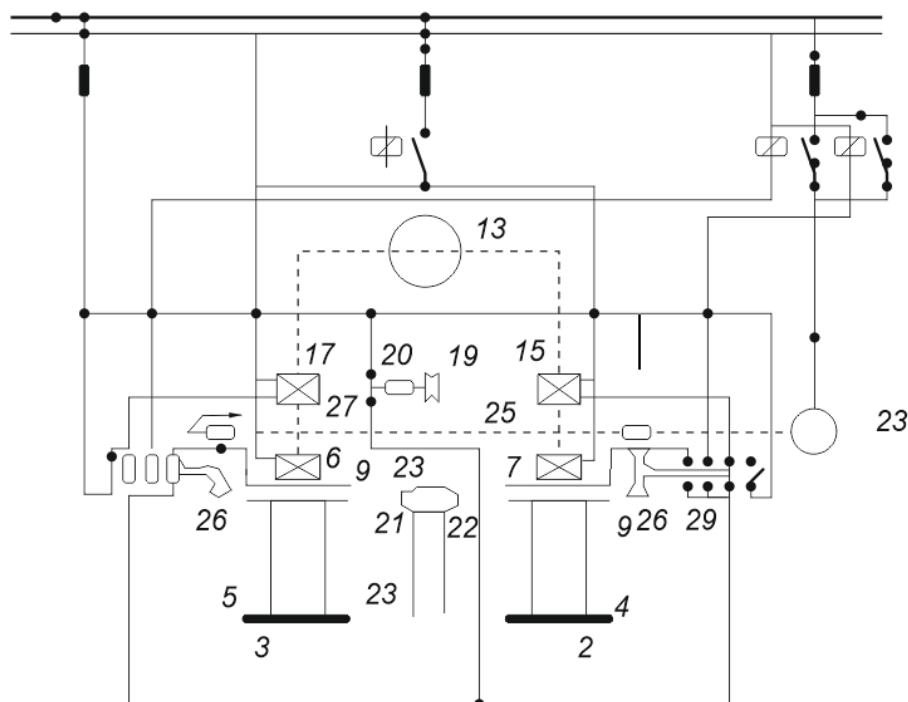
Устройство непрерывной намотки на катушки металлической проволоки
